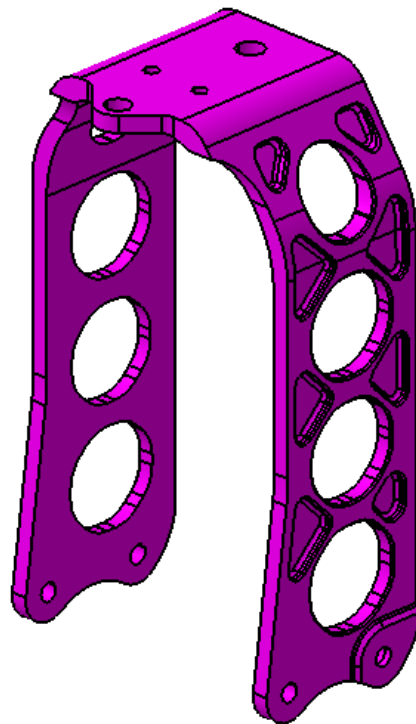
Diseño final de la horquilla de dirección MT2-DI-03-01.
